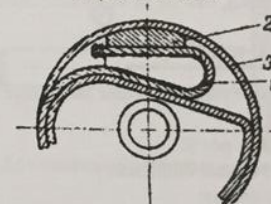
Prinderea pe tambur: 1 - cablu; 2 - pană; 3 - carcasă de fixare.
